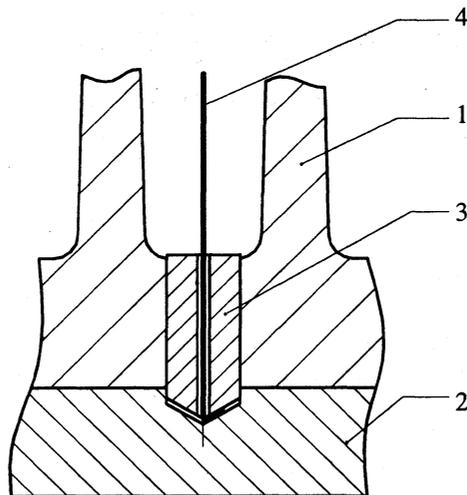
Принцип изготовления термопары: 1 – ребра цилиндра (алюминиевый сплав); 2 – гильза цилиндра (чугун); 3 – поршень (алюминий); 4 – константановый провод
